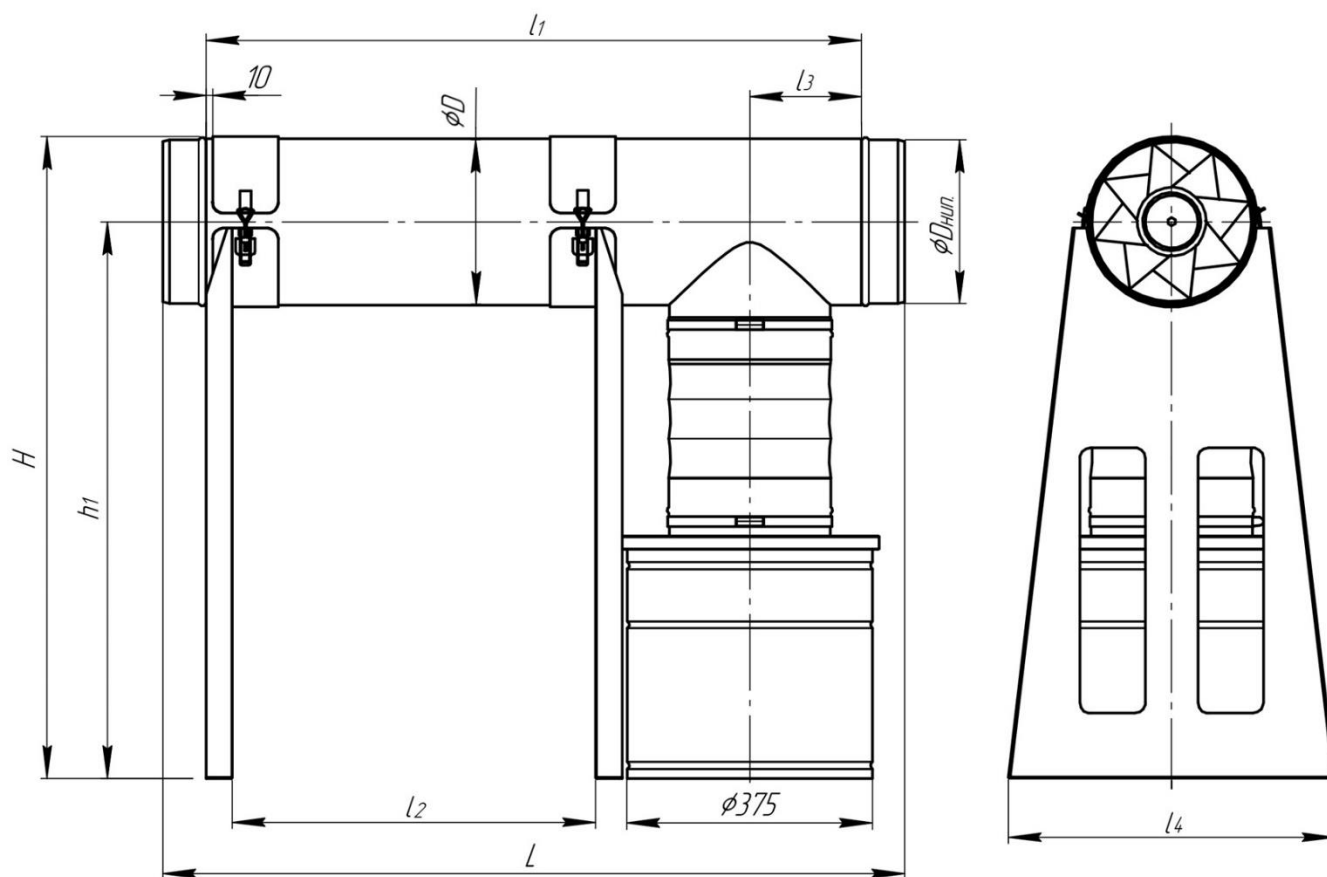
Габаритные размеры циклонов ЦПО-1000, ЦПО-2500, ЦПО-4000, ЦПОу-1000, ЦПОу-2500, ЦПОу-4000 (для моделей ЦП-1000, ЦП-2500, ЦП-4000, ЦПу-1000, ЦПу-2500, ЦПу-4000 без учёта опор)
